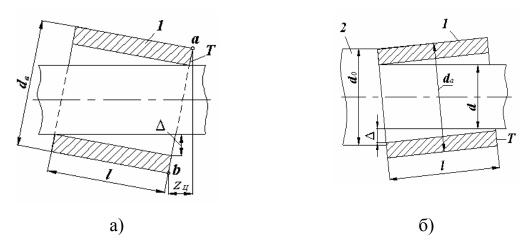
Варианты базирования детали на валу: а — по цилиндрической поверхности; б — по торцу
